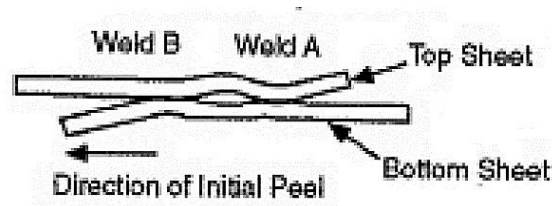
Pruebas en Soldadura por Fusión
